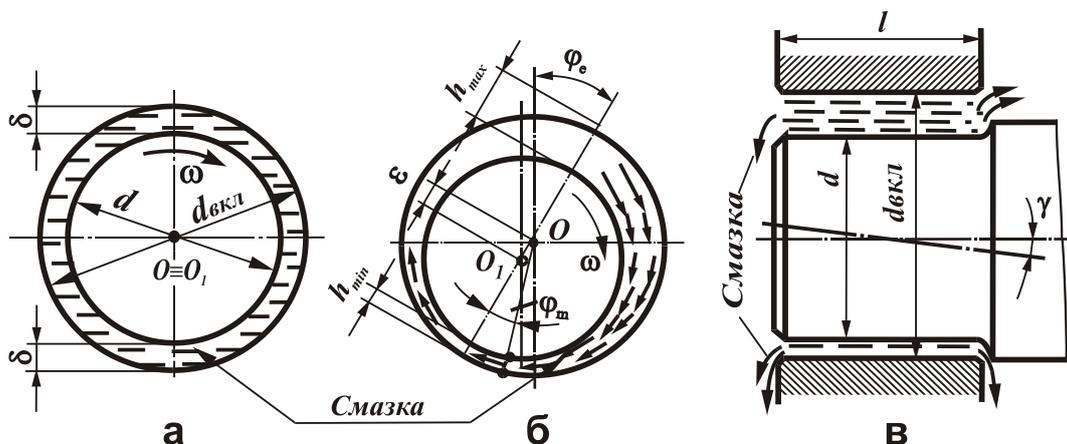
Схема параметров подшипника: а – идеальное положение осей вкладыша и цапфы; б, в – реальное расположение вала во вкладыше подшипника [3]
